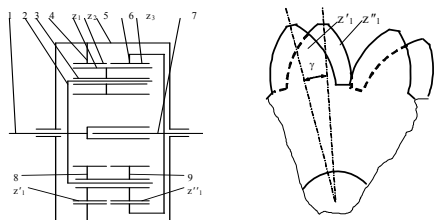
Схема многопоточного планетарного эксцентрикового редуктора с одно (3) и двухвенцовыми (8,9) сателлитами
